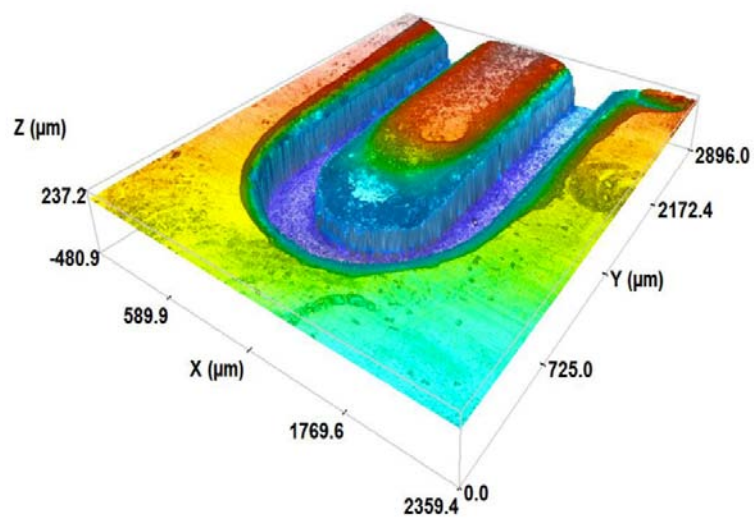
34 Elemento a U – Componente stampato da inserto fresato - C
